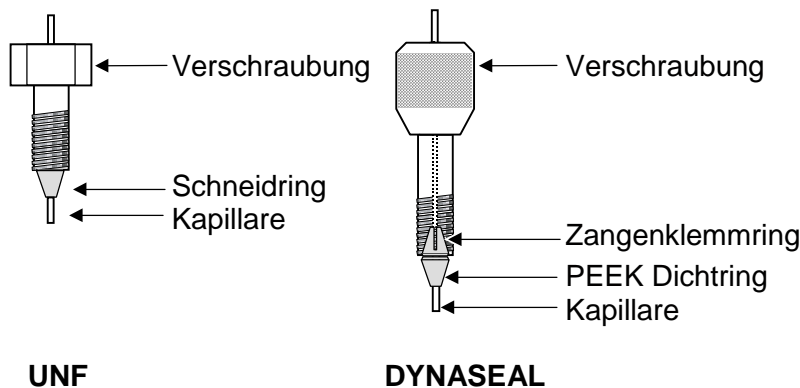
Prinzip der UNF- und DYNASEAL-Verschraubungen
